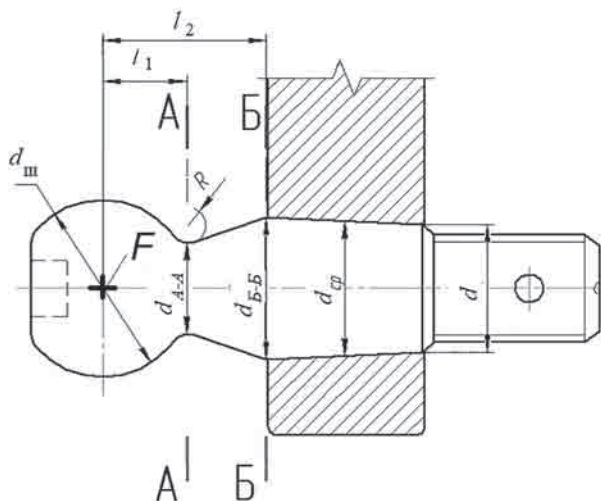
Расчетная схема шарового пальца рулевого механизма
